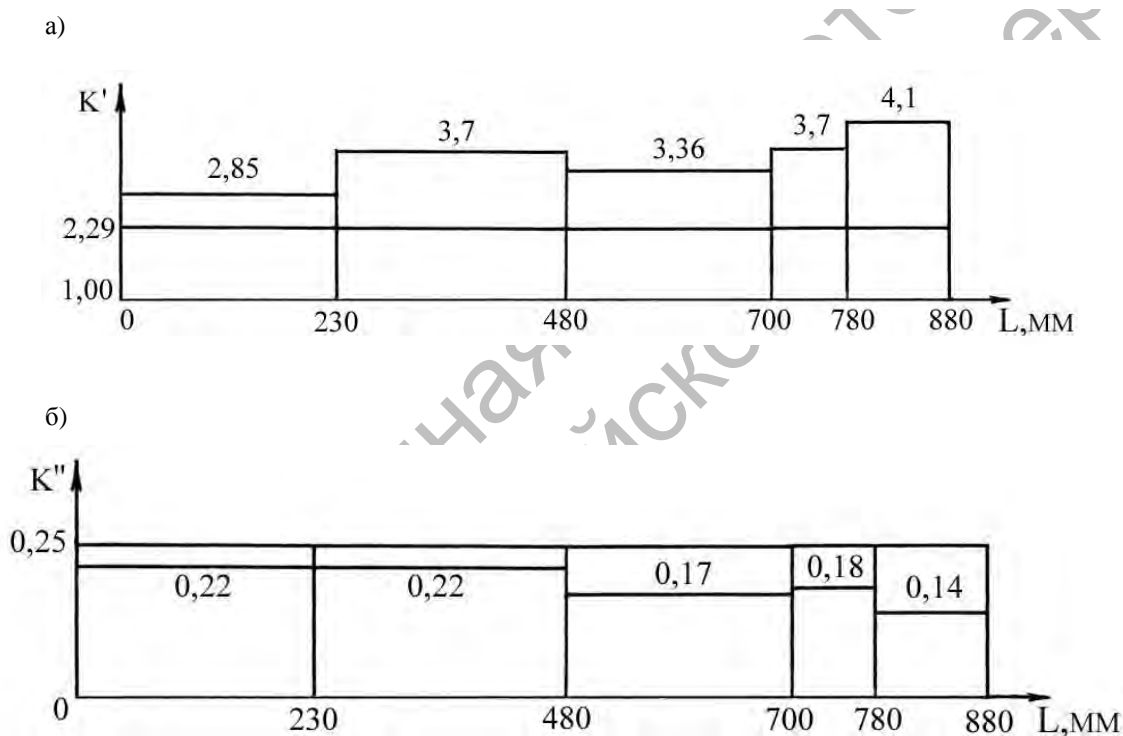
Запас устойчивости ПКП заготовки шарового пальца: а – по критерию K' от потери сцепления заготовки с инструментом; б – по критерию K'' от разрыва заготовки
